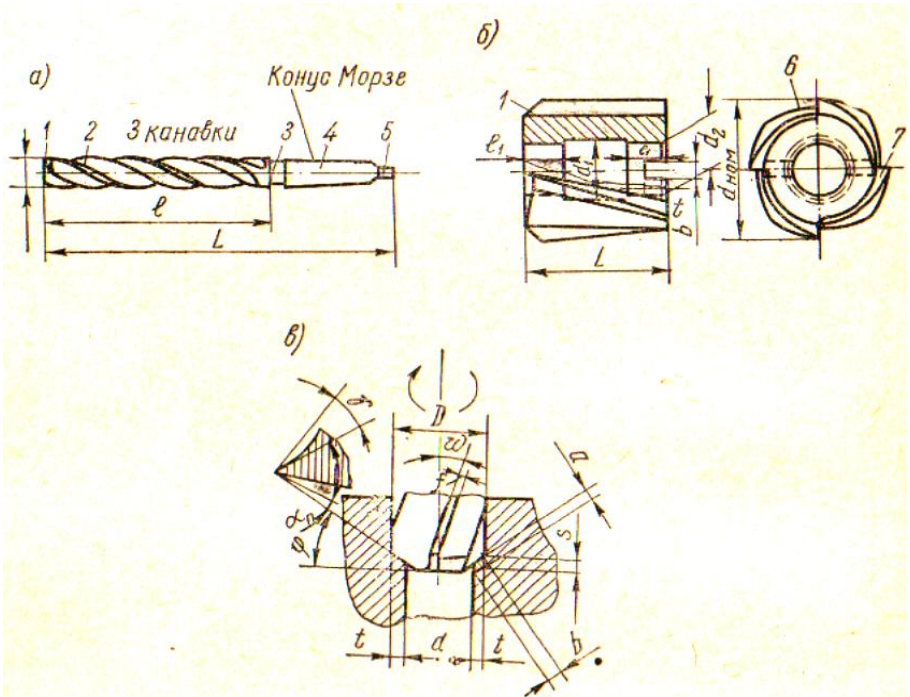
Элементы зенкера и схема резания: а – элементы цельного зенкера; 1 – режущая (заборная) часть; 2 – ленточка; 3 – шейка; 4 – хвостовик; 5 – лапка; б – насадной зенкер; 6 – канавка; 7 – режущее лезвие; в – схема резания; t – глубина резания; ϕ – угол в плане; ω – угол наклона винтовых канавок; α_n – нормальный задний угол; γ – передний угол
